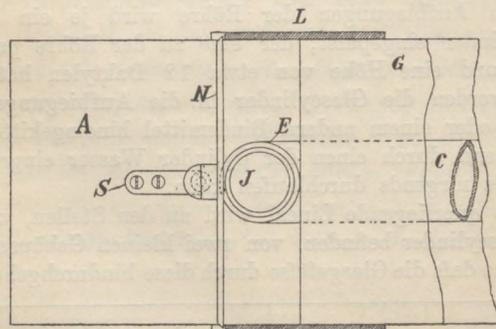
b. Nivellierlineal (Grundriss).
